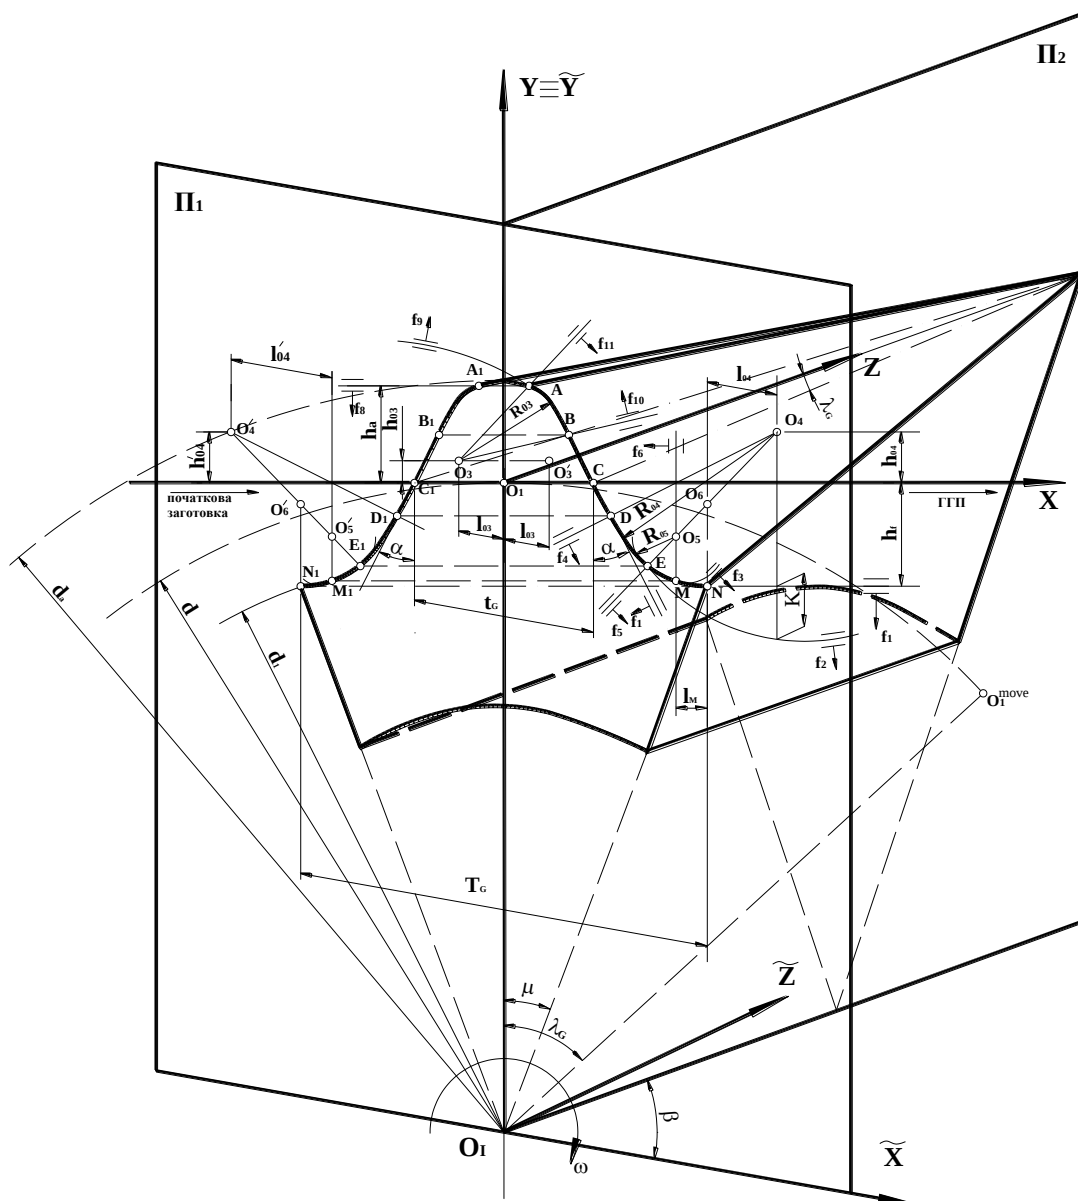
Розрахункова схема інструмента для виготовлення ГПП
